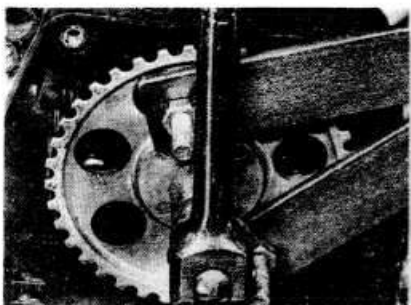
Импровизированное приспособление для удерживания в неподвижном положении звездочки распредвала
